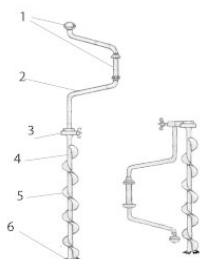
Ручной шнековый ледобур (складной) в рабочем и транспортном положении: 1 – рукоятки; 2 – коловорот; 3 – шарнирное соединение с барашковой гайкой; 4 – шток; 5 – шнек; 6 – режущая часть.
